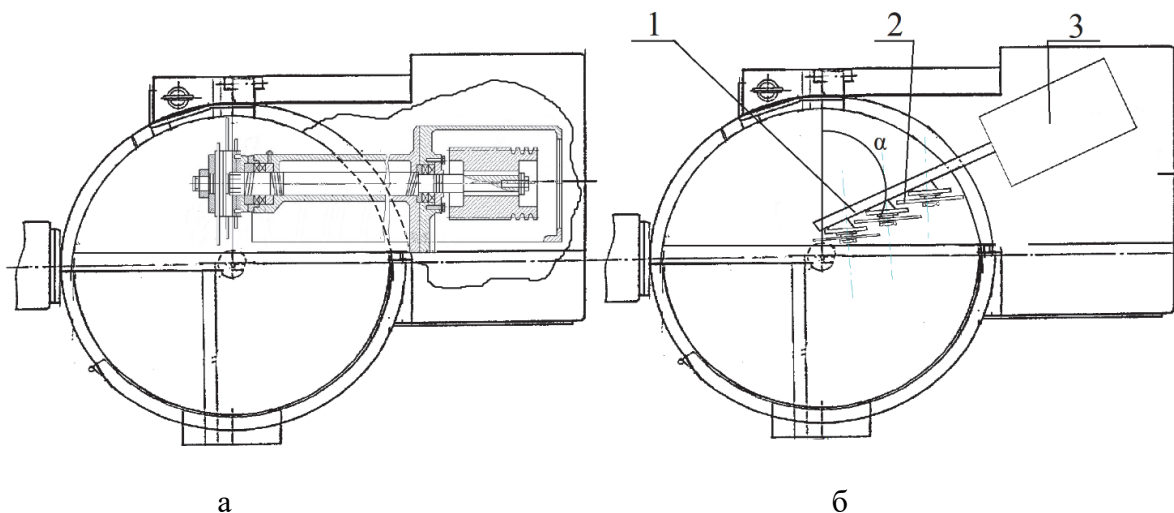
Реконструкция куттера: а – прототип, б – изменённый режущий рабочий орган машины: 1 – узел режущего рабочего органа; 2 – ножевой пакет; 3 – шкаф электрооборудования и передач; α – результирующий угол поворота лезвий
